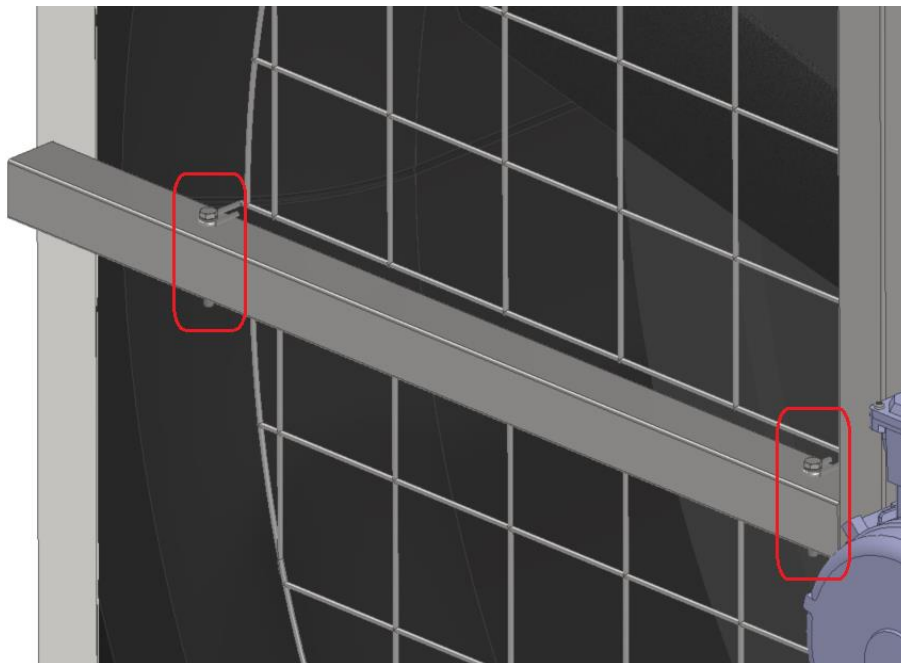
Conexión pernada: malla del lado de succión - estructura metálica.
